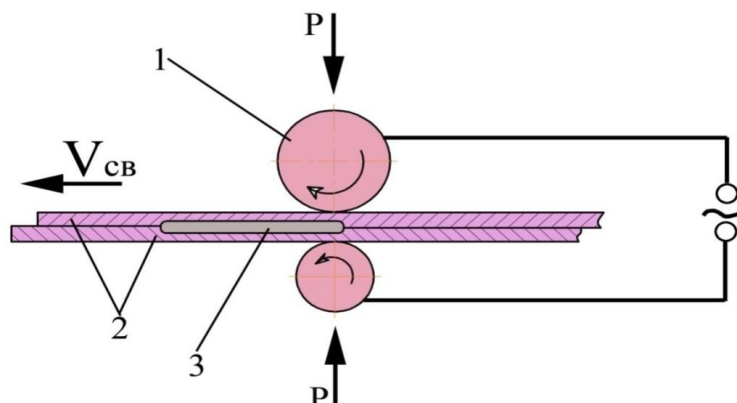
Сущность процесса шовной сварки: 1 – сварочные электроды (ролики); 2 – свариваемые изделия; 3 – сварной шов
